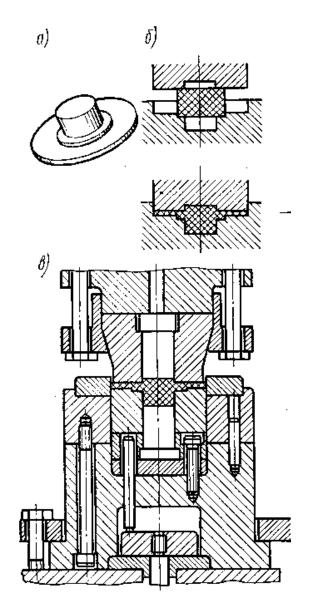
Схема деформирования и конструкция штампа для закрытой штамповки поковок с тонкими полотнами на высокоскоростных молотах: а – конфигурация поковки; б – схема деформирования; в – конструктивная схема штампа
